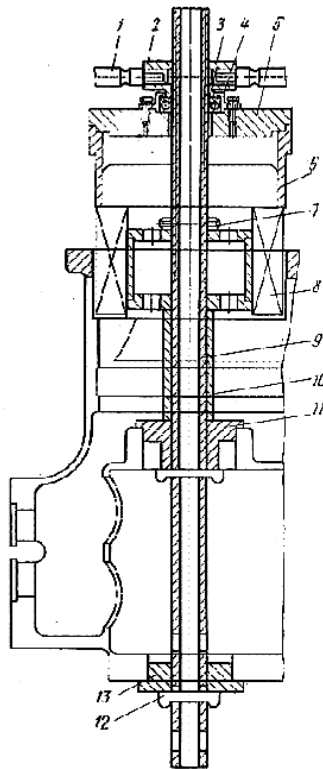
Приспособление для запрессовки статора в блок-картер бессальникового компрессора:
